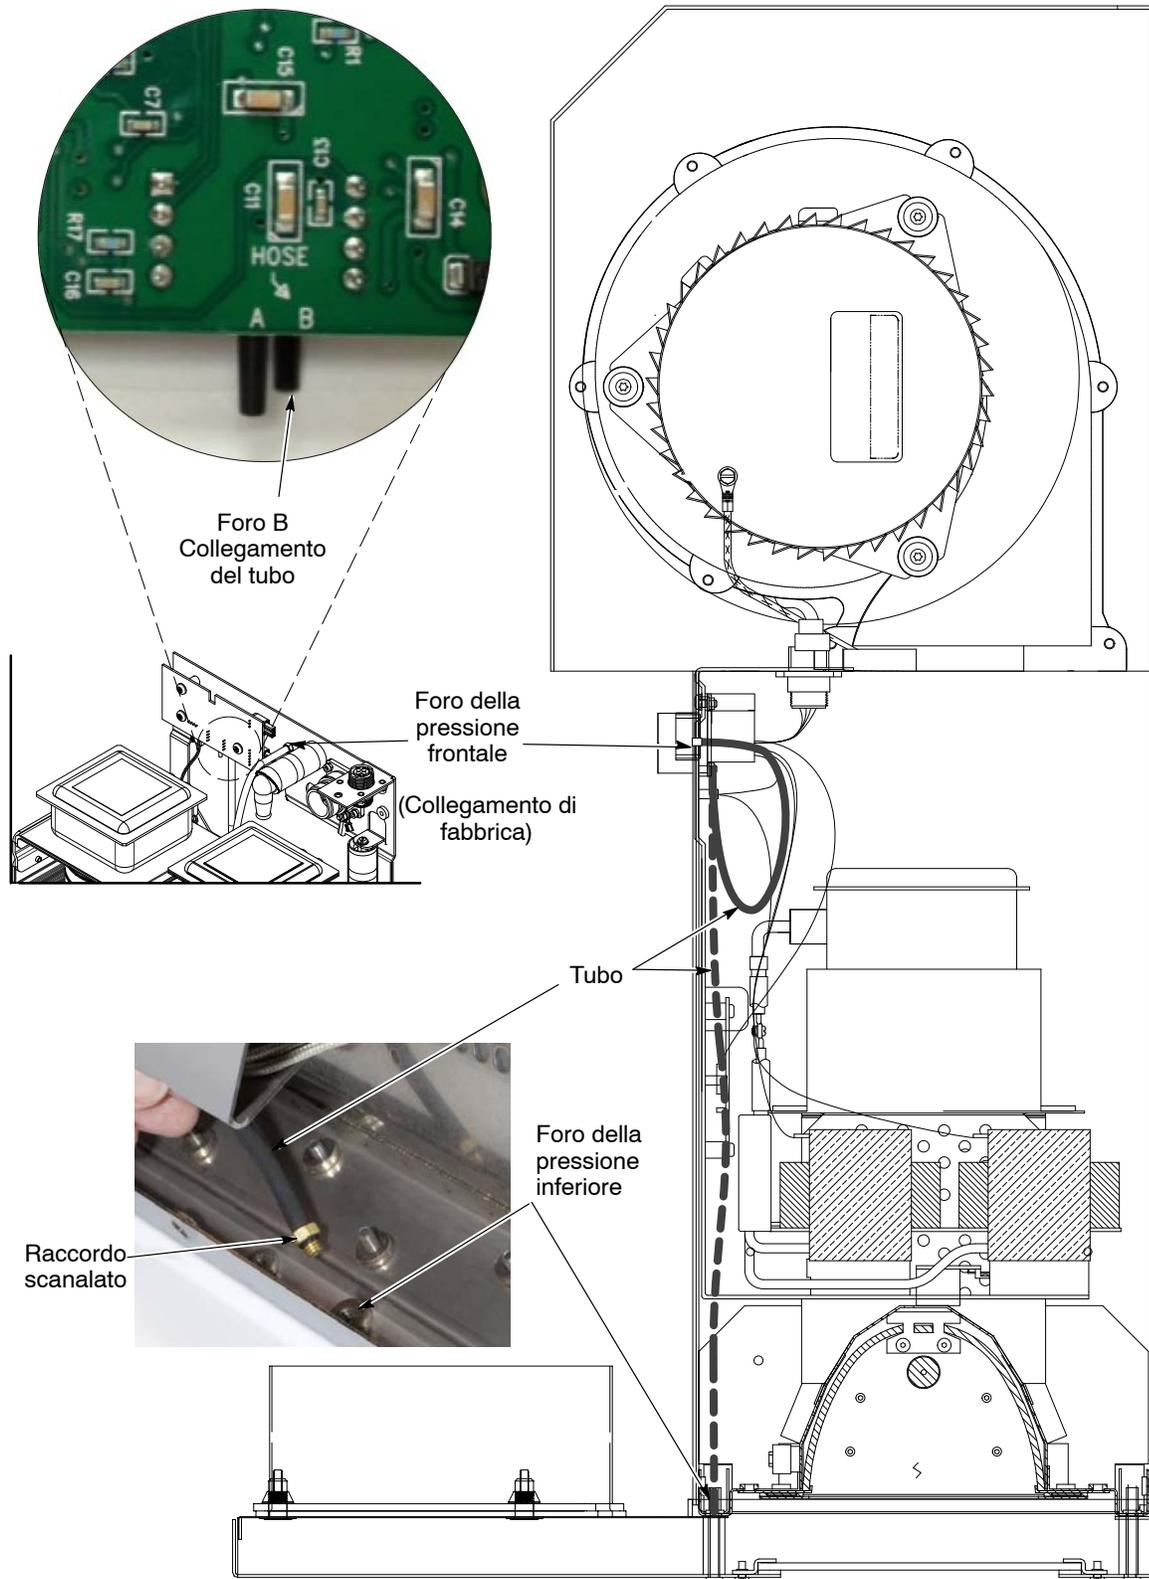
Collegamenti dei fori della pressione – versione con soffiante interno
